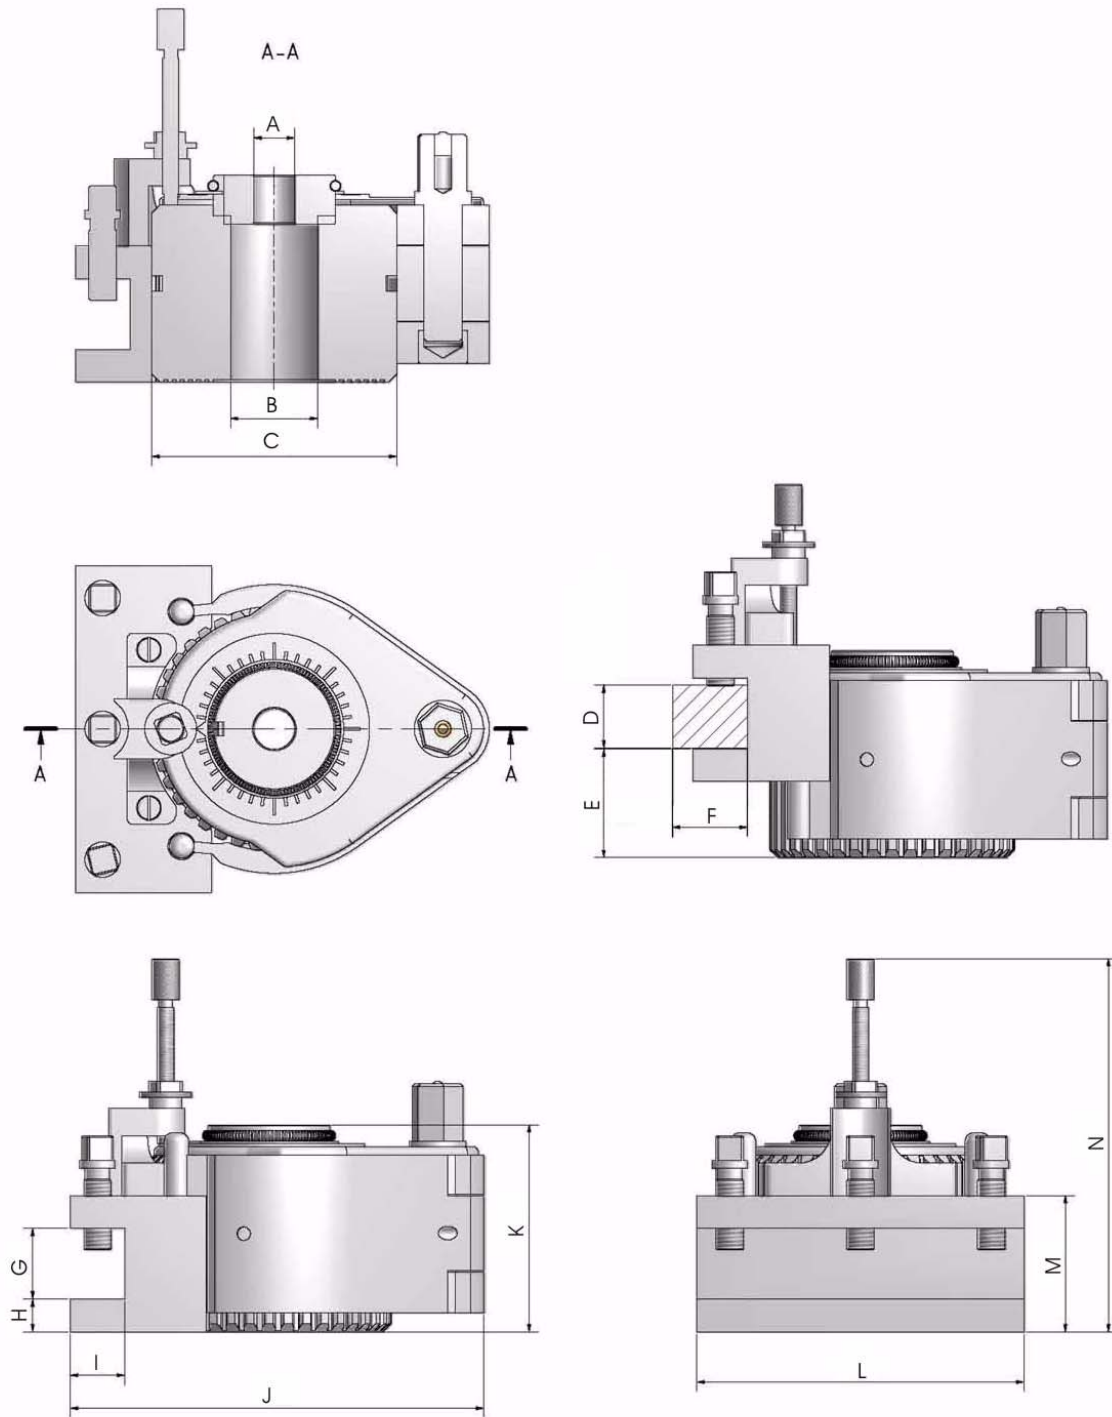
Stahlhalter für Vierkantmeißel - Tool holder for square tool
